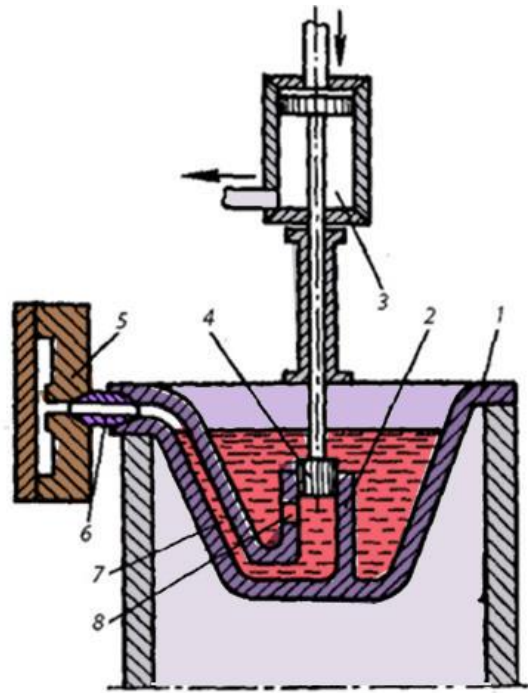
Схема поршневої машини з гарячою камерою пресування
